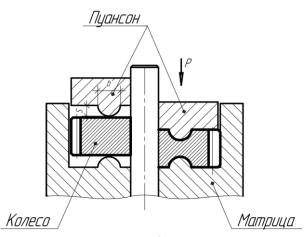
Схема восстановления зубчатого колеса выдавливанием
